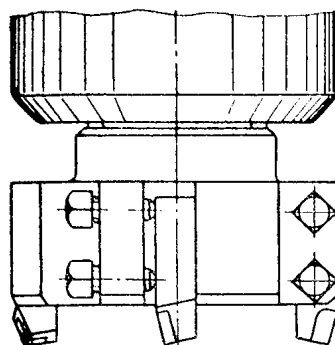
Фреза, оснащенная твердым сплавом, с крепление зубьев винтами
